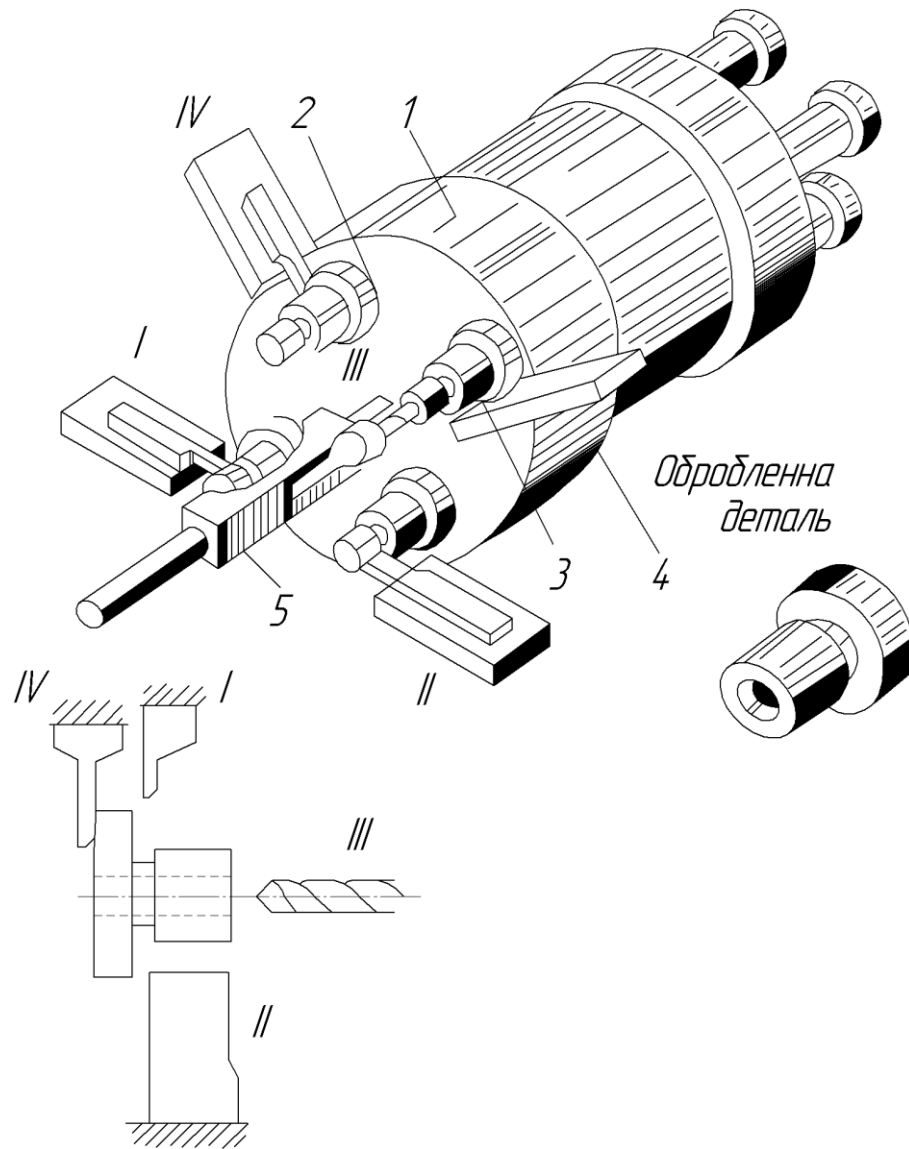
Схема обробки деталі на багатошпindelьному напівавтоматі
